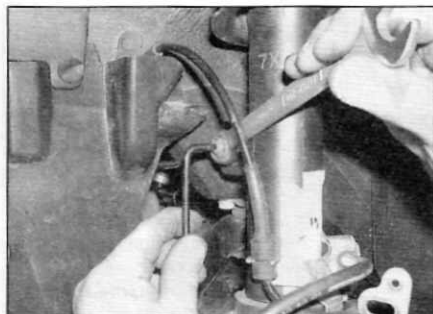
Отверните гайку крепления стойки стабилизатора к стойке подвески
